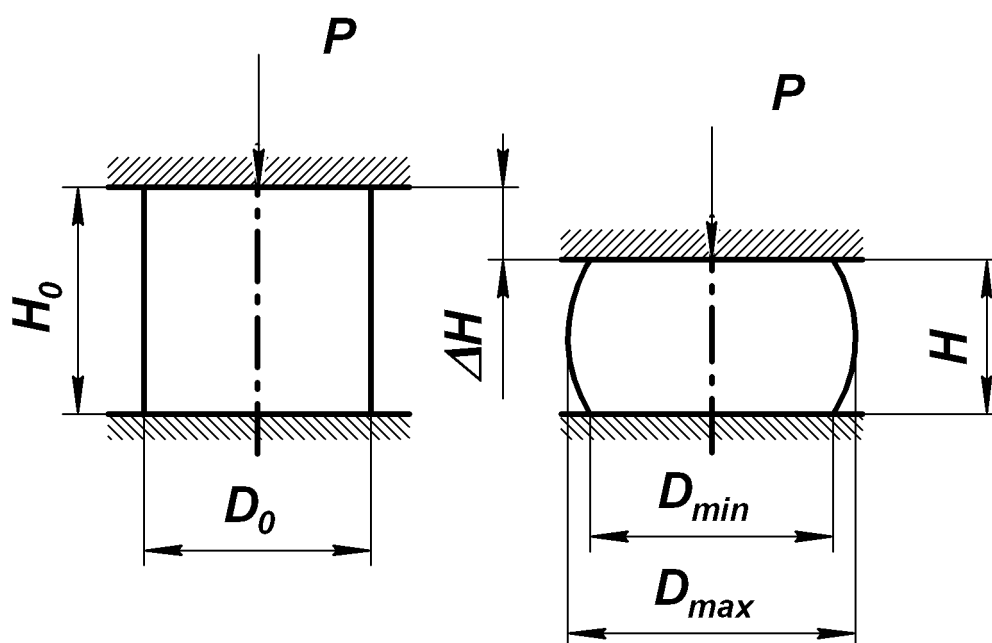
Цилиндрическая заготовка до осадки и после осадки
